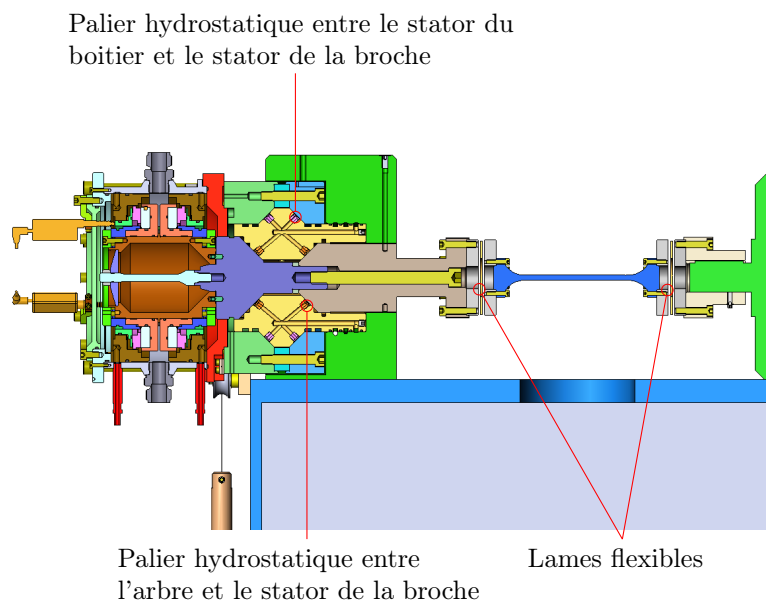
Vue en coupe du banc d'essai
